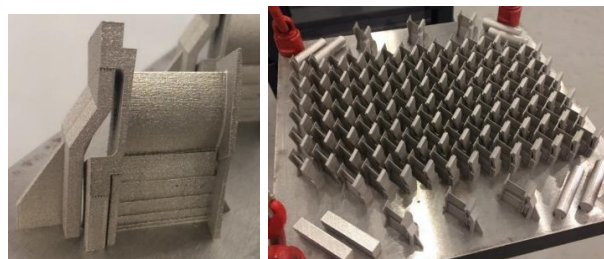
Деталі типу лопатка зі сплаву Inconel 718
